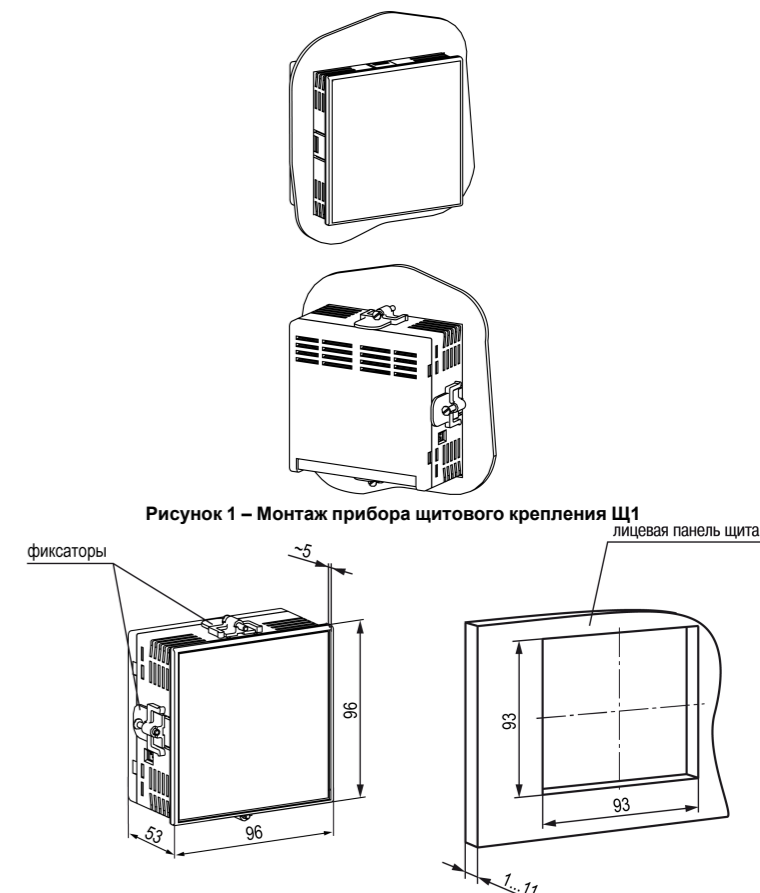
Габаритные размеры корпуса Щ1 и монтажного отверстия в щите
